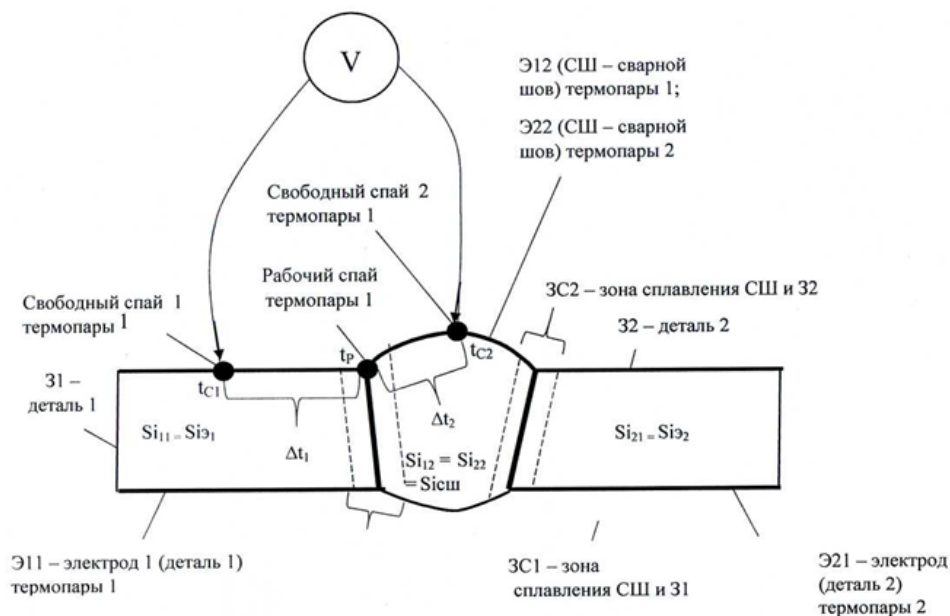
Схема открытого формирования ТЭДС с нагревом наружной стороны сварного соединения стальных обшивок судов поперек шва
